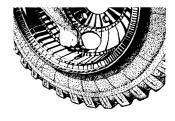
Установка прямой лопатки в прорезь бортового кольца
